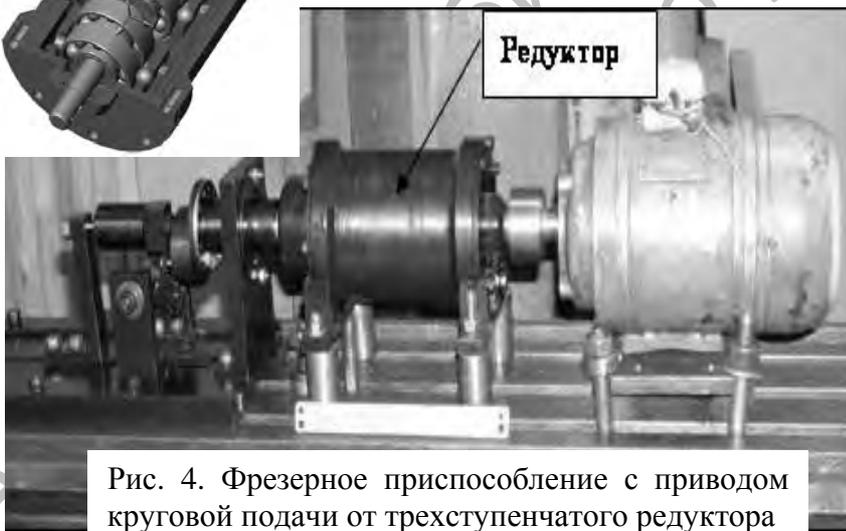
Фрезерное приспособление с приводом круговой подачи от трехступенчатого редуктора
